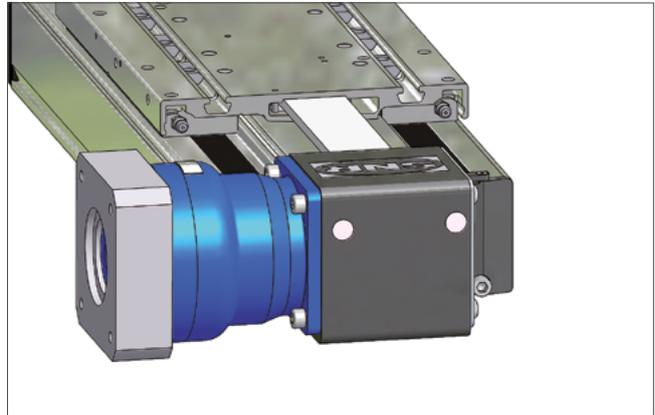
AXDL mit integriertem Planetengetriebe
